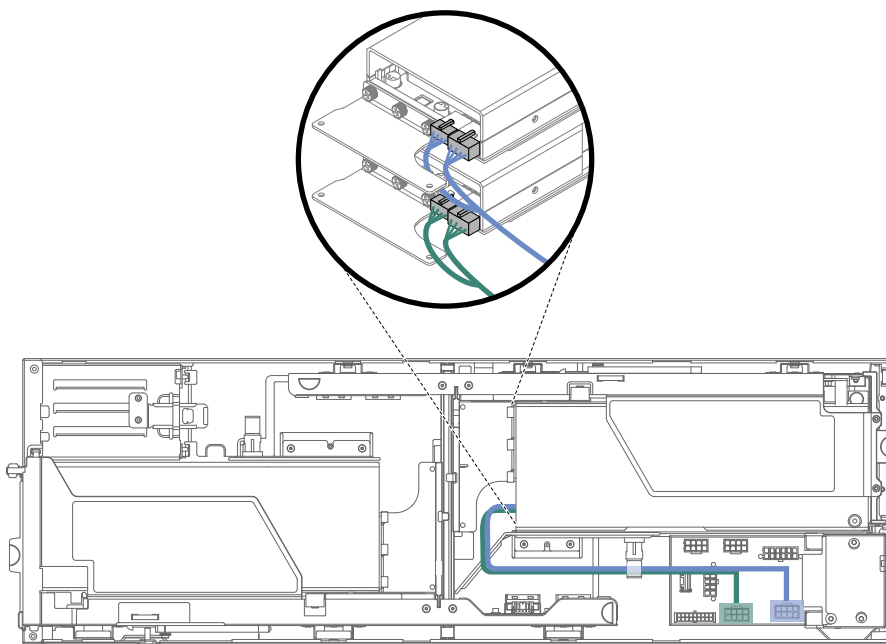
Adaptadores GPU do conjunto do PCI traseiro com conexão do cabo de alimentação da placa GPU
